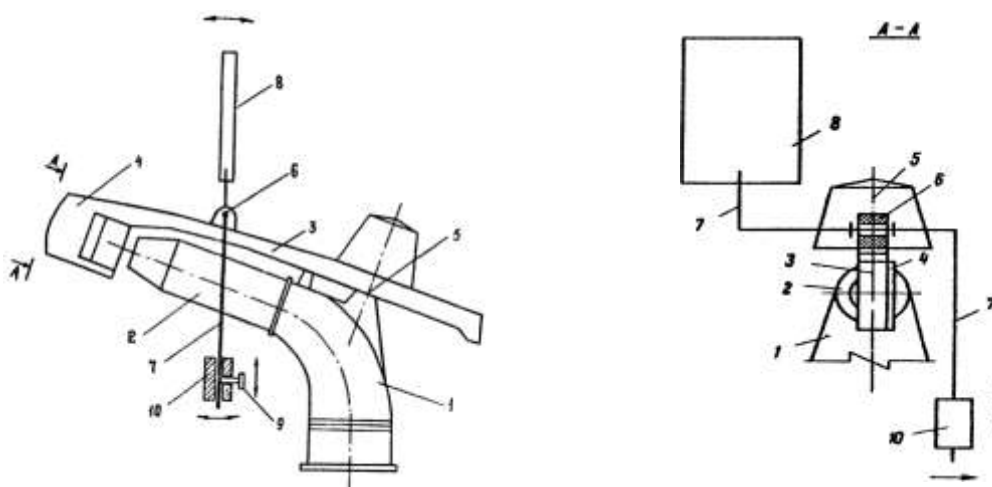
Дождевальная установка с передним расположением паруса-датчика: 1 – корпус; 2 – ствол; 3 – коромысло; 4 – реактивная лопатка; 5 – ось вращения коромысла; 6 – шарнир; 7 – изогнутая ось; 8 – парус-датчик; 9 – фиксирующий винт; 10 – противовес [9]
